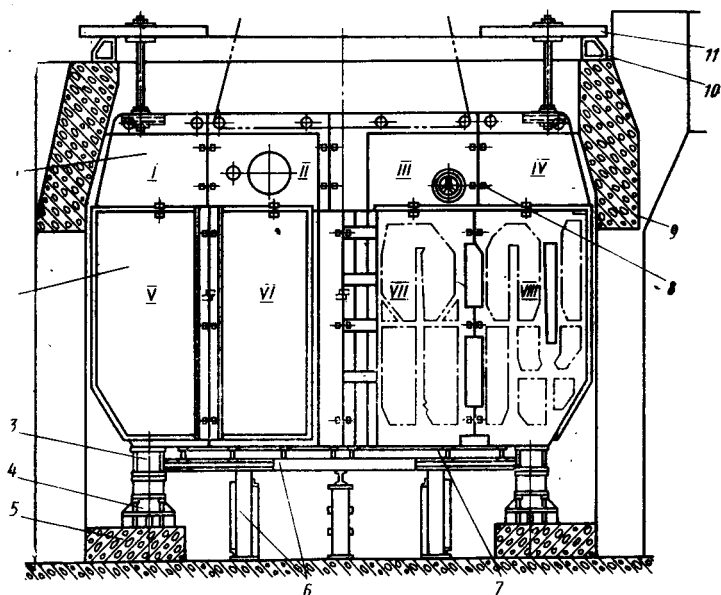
Схема установки и сборки корпуса конденсатора турбины К-300-240 в проеме фундамента:
